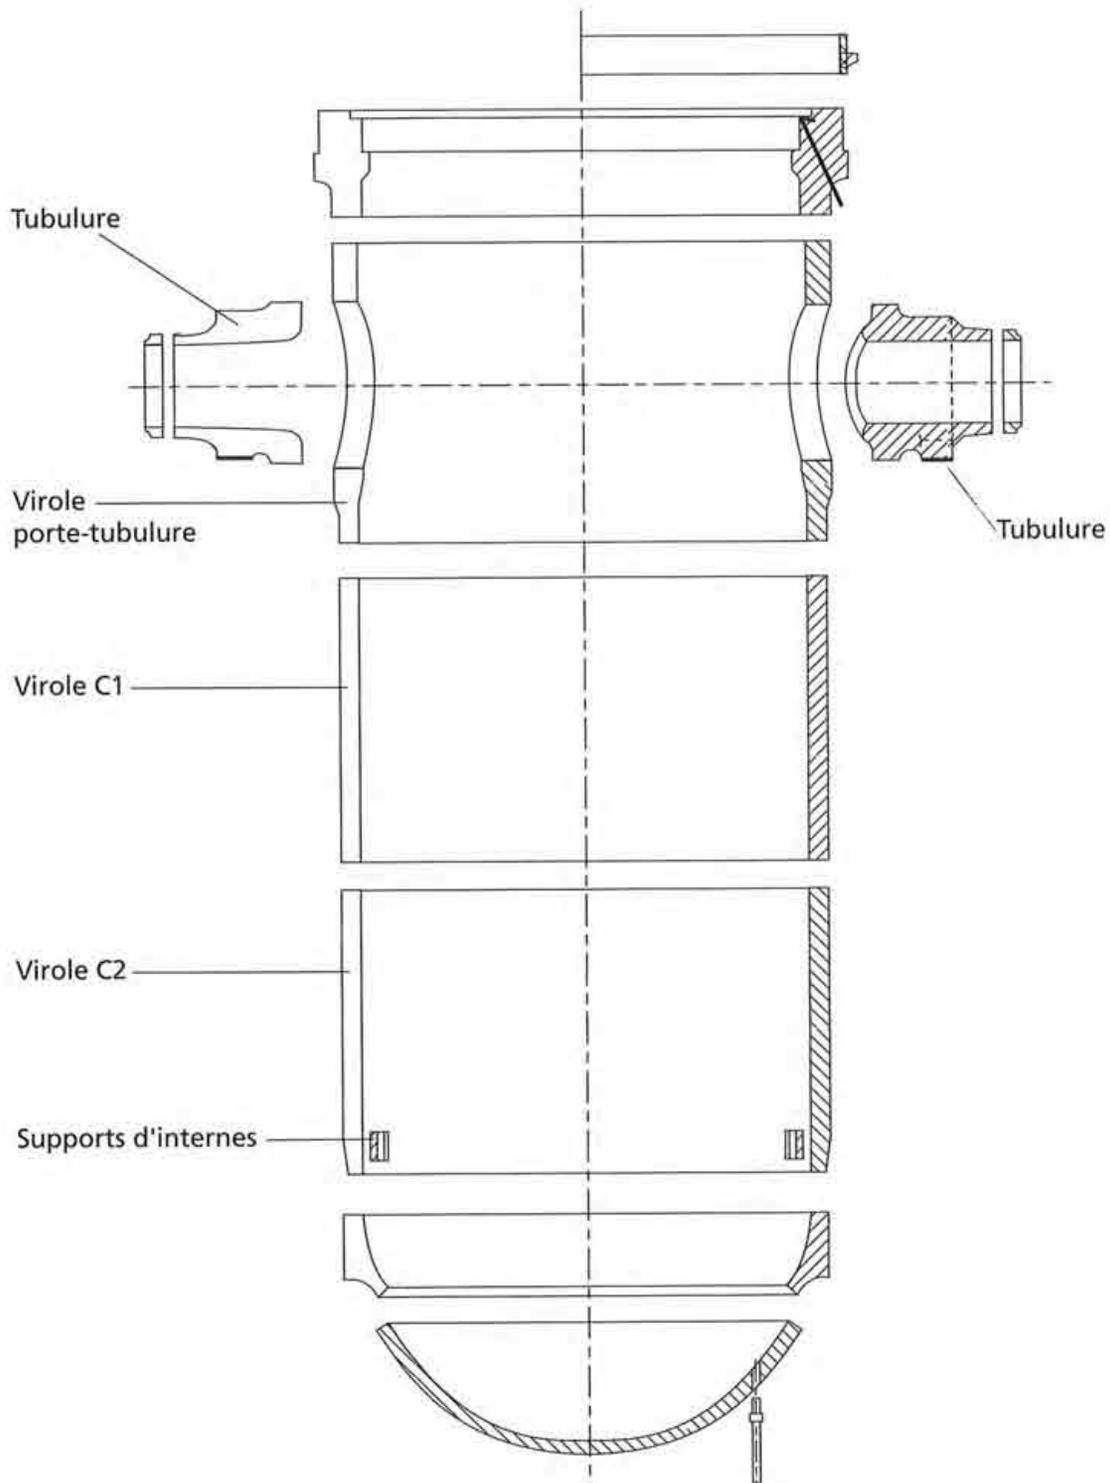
Les composants d'une cuve (sans couvercle) avant son assemblage. Les parties les plus irradiées sont les viroles C1 et C2 et la soudure qui les assemble. Chacune d'elle mesure environ 4 mètres de diamètre et 20 cm d'épaisseur. (Source : Framatome)
